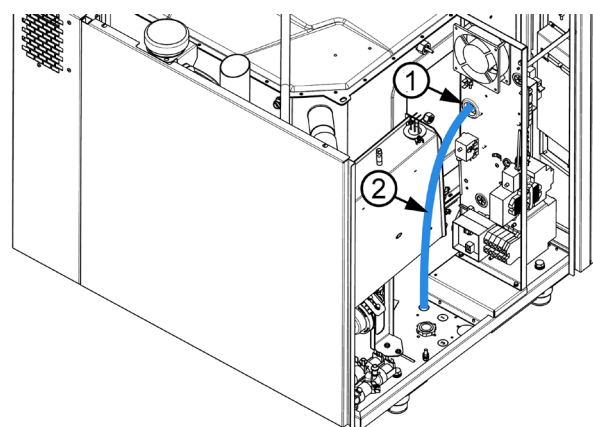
Passage du câble UTP par l'œillet en caoutchouc
